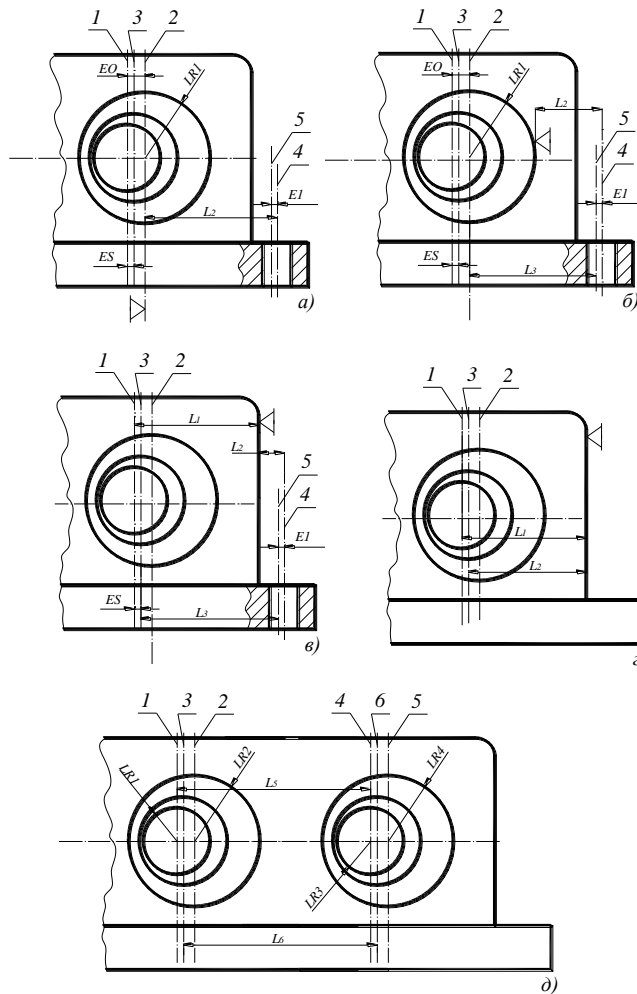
Основні варіанти базування корпусних деталей на верстатах при механічній обробці в напрямку осі координат  $OX$
